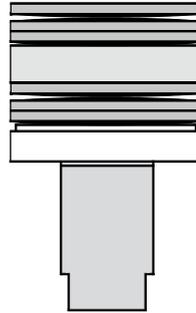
Montaje correcto del adaptador de válvula al actuador AEL56
